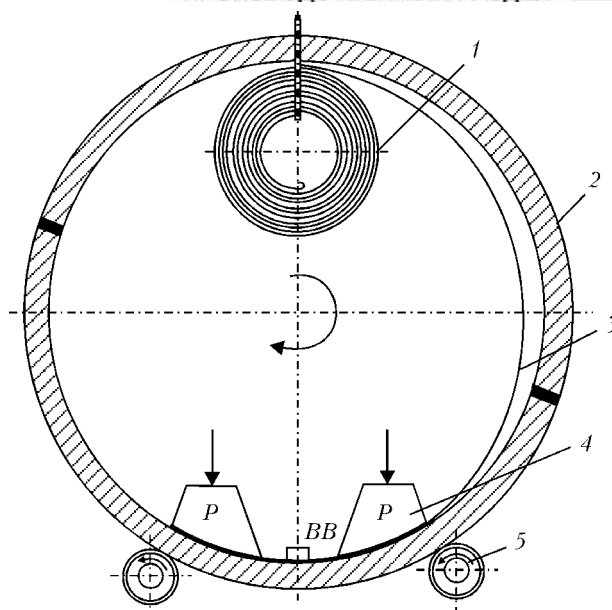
Принципиальная схема плакирования внутренней поверхности цилиндрических сосудов с использованием сварки взрывом: 1 — рулон, свернутый из полотна плакирующего металла; 2 — корпус сосуда; 3 — полотно плакирующего металла; 4 — прижимы; 5 — роликовый стенд
